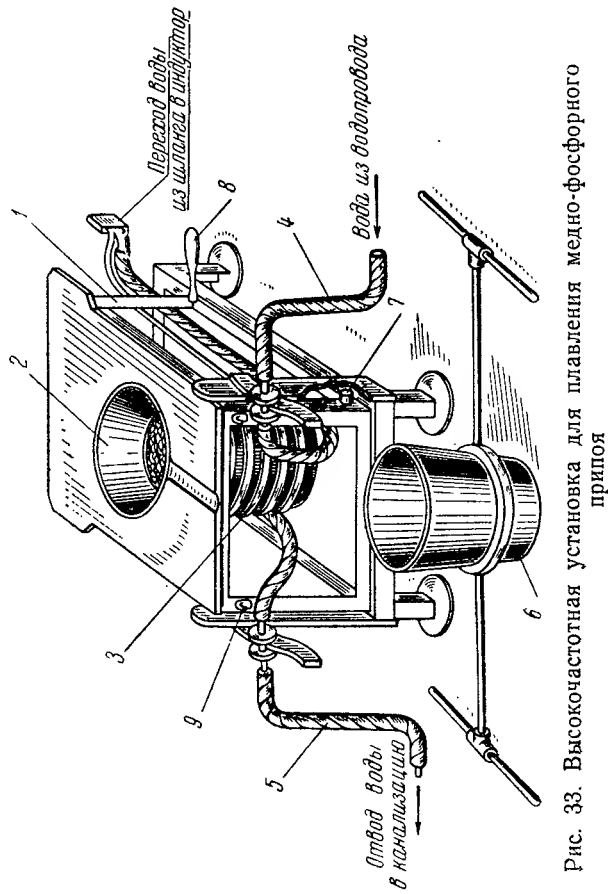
Высокочастотная установка для плавления медно-фосфорного припоя
